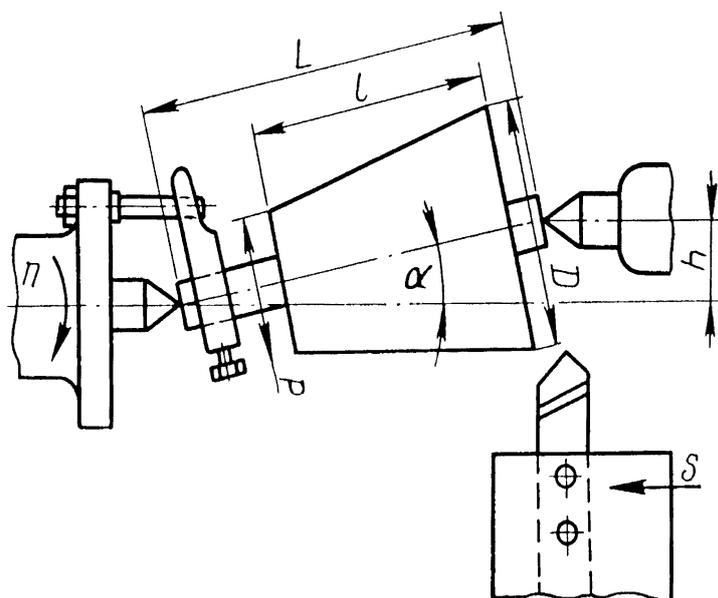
Обработка конической поверхности путём смещения центра задней бабки
